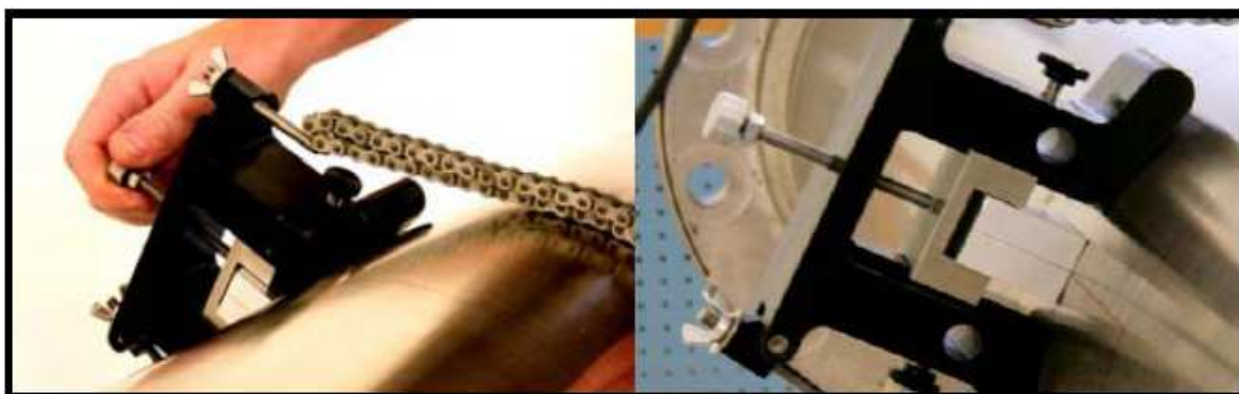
Установка положения удерживающей скобы приспособления CFG-PI
